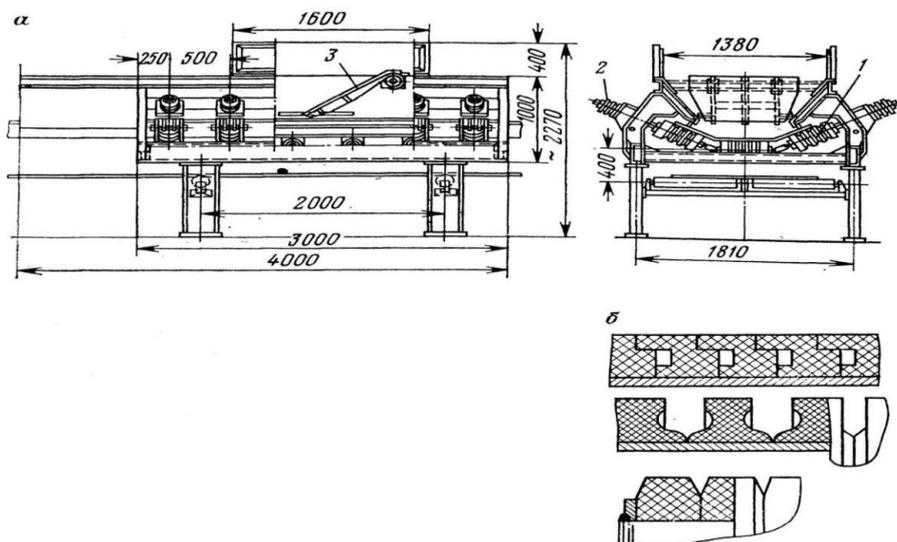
Загрузочная секция подземного ленточного конвейера: а - с подвесными шарнирными роlikоопорами; б - различные конструкции футеровок роlikов; 1 - шарнирными роlikоопора; 2 - резиновые амортизаторы; 3 – лоток
